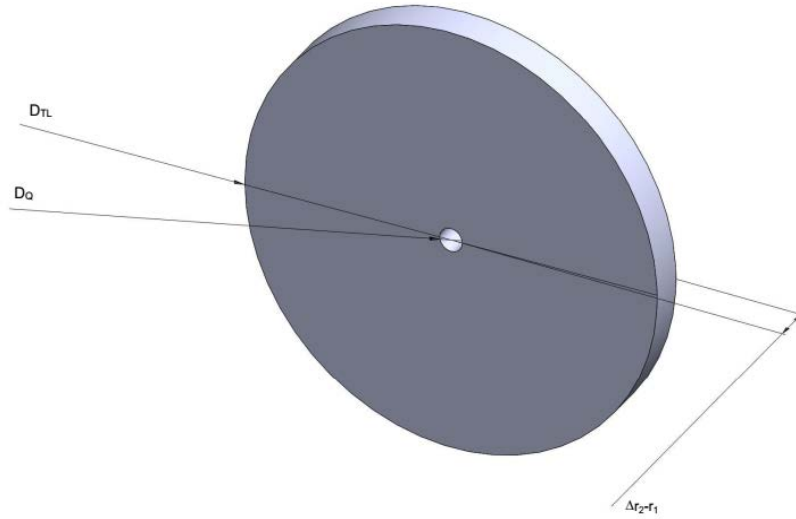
, Dimensiones de la tapa de ladrillo refractario adyacente al quemador
